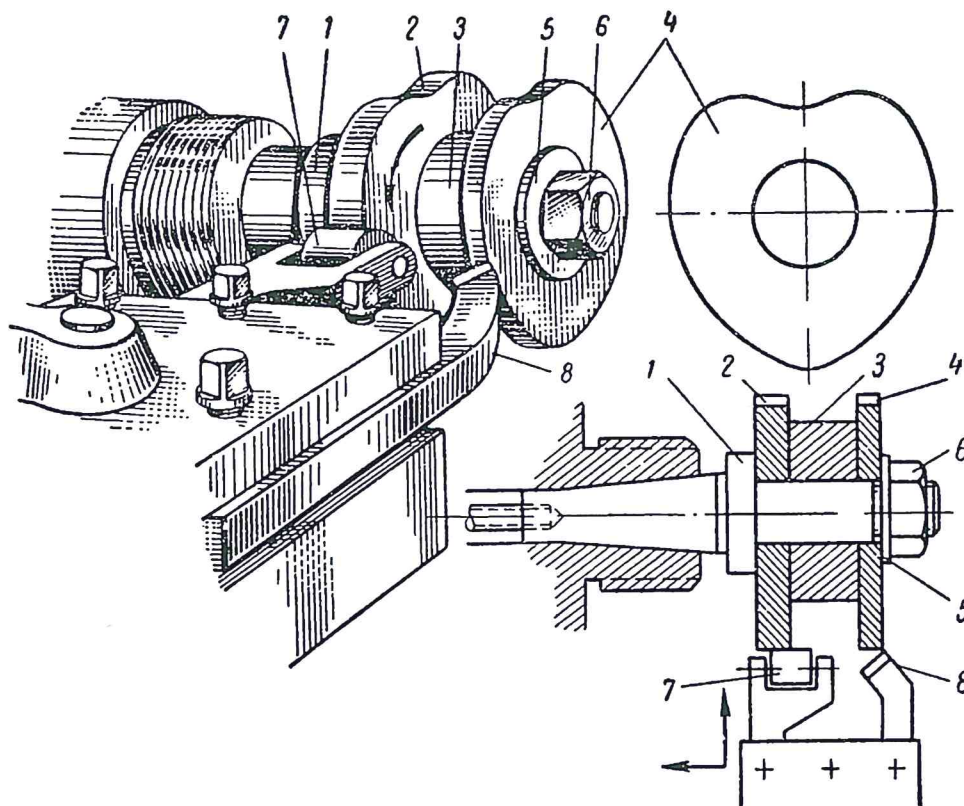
Обтачивание профиля дискового кулачка по копиру (предложение т. Конышева)
